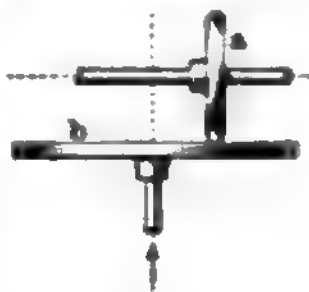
Planrad und Rad mit balliger Umfangsfläche.
